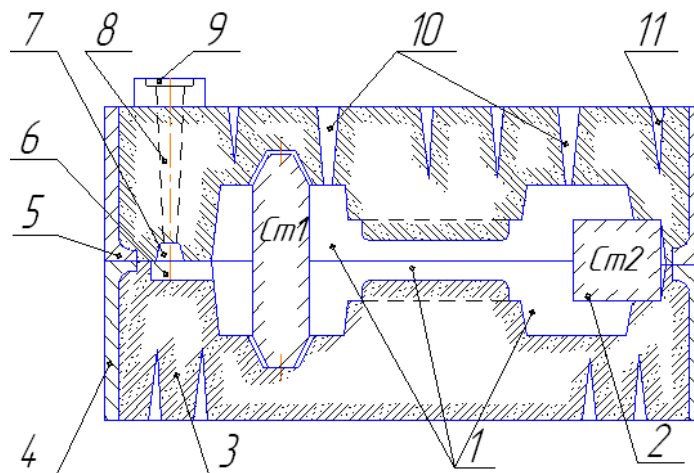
Ливарна форма для отримання виливка важеля:
